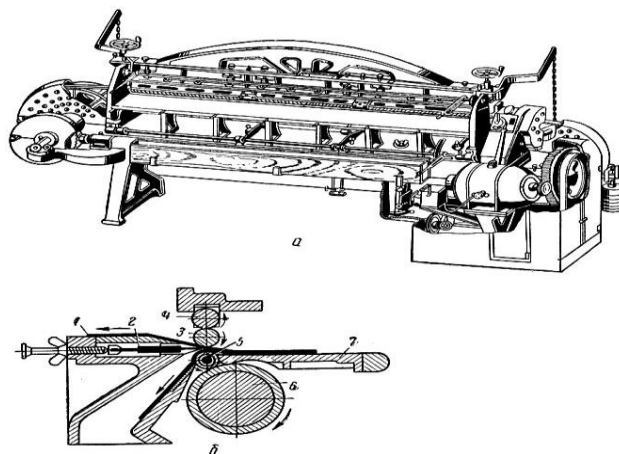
Двоильно-ленточная машина: а - общий вид; б - схема рабочих органов; 1 - полуфабрикат; 2 - ленточный нож; 3 - рифленый подающий вал; 4 - прижимной вал; 5 - кольцевой подающий вал; 6 - обрезающий вал; 7 - стол
